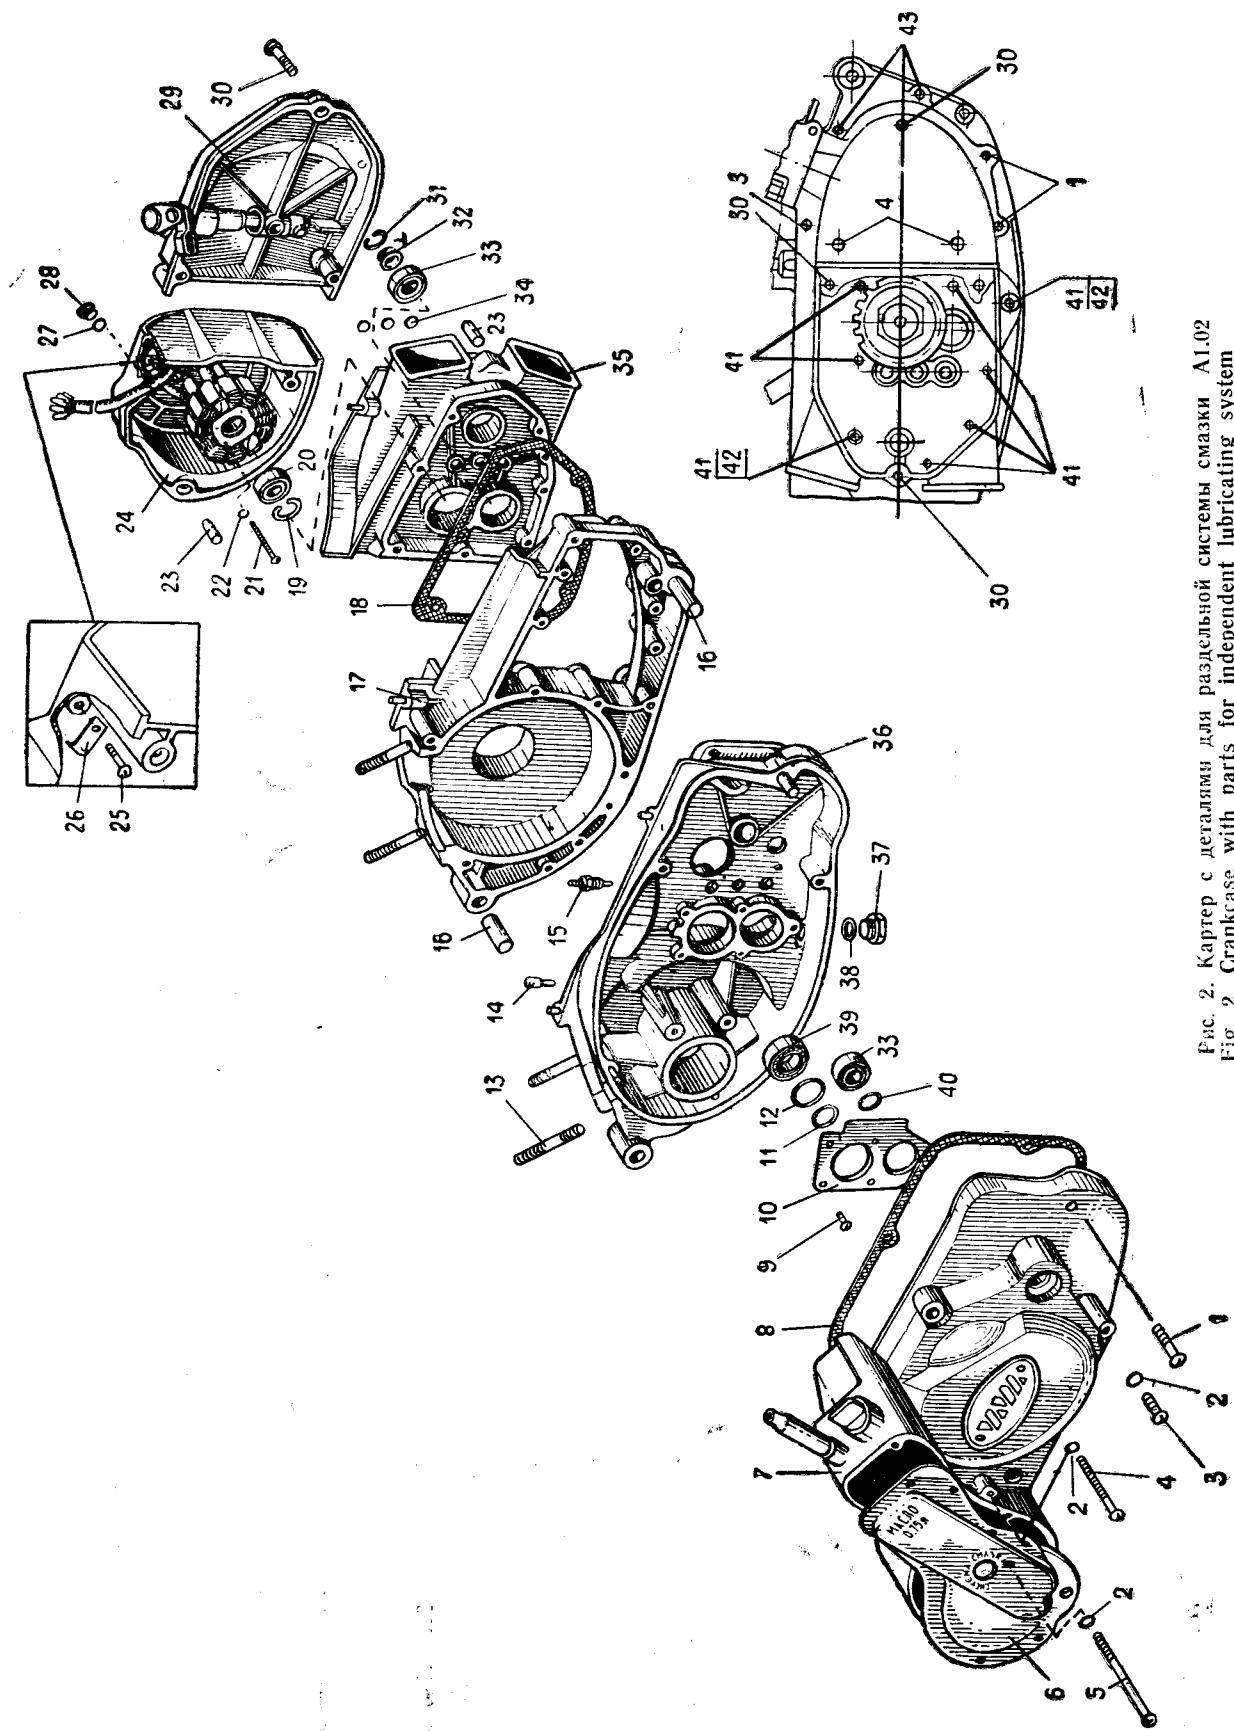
Картер с деталями для раздельной системы смазки А1.02
